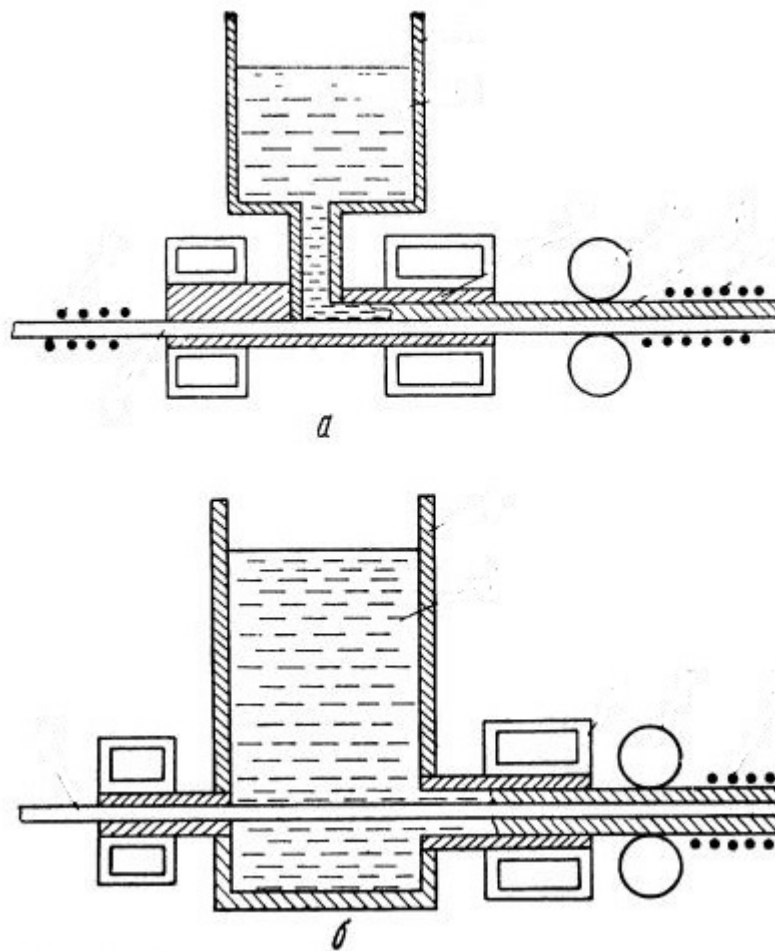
Схема виготовлення композиційних заготовок плоского (а) та круглого (б) перерізу безперервного литва [1]
